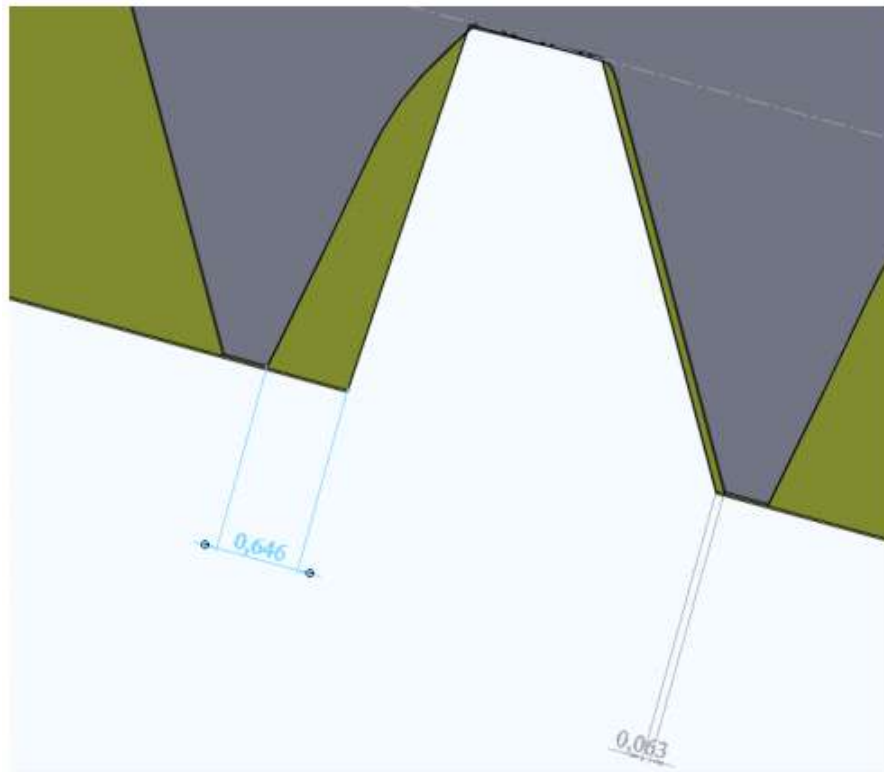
Исходный профиль заготовки и получаемый фрезой [14, с. 545]
